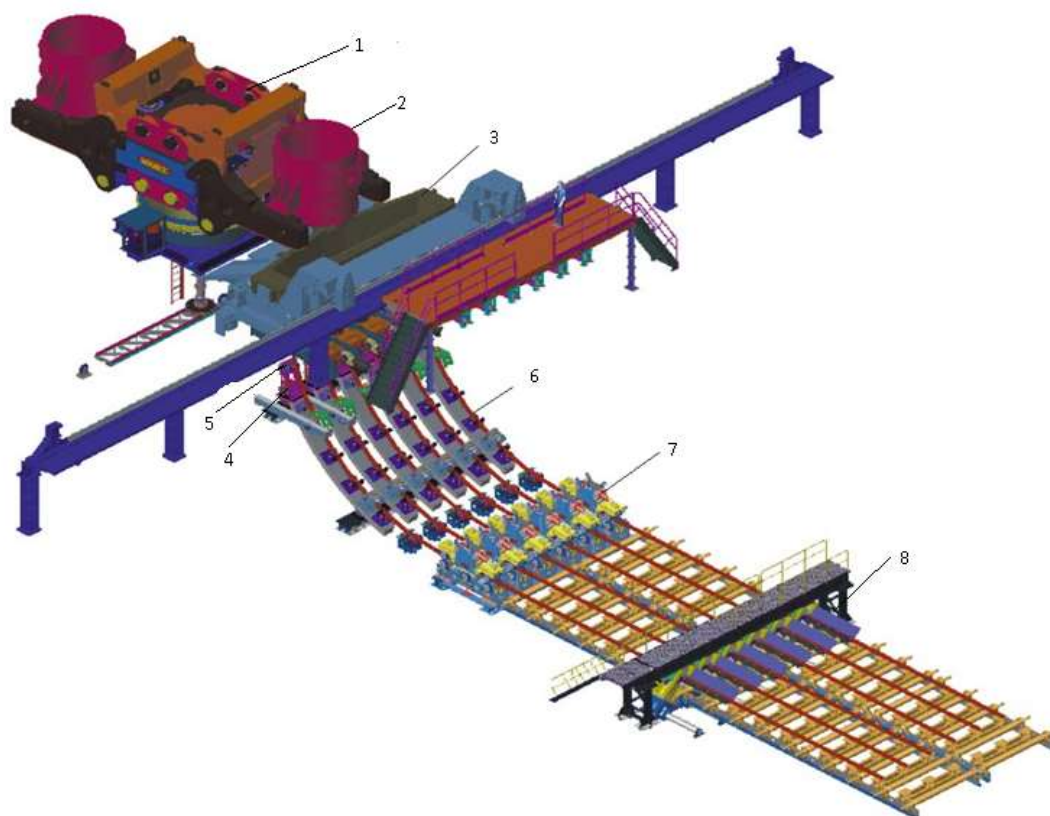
Общая схема разливки стали на МНЛЗ
